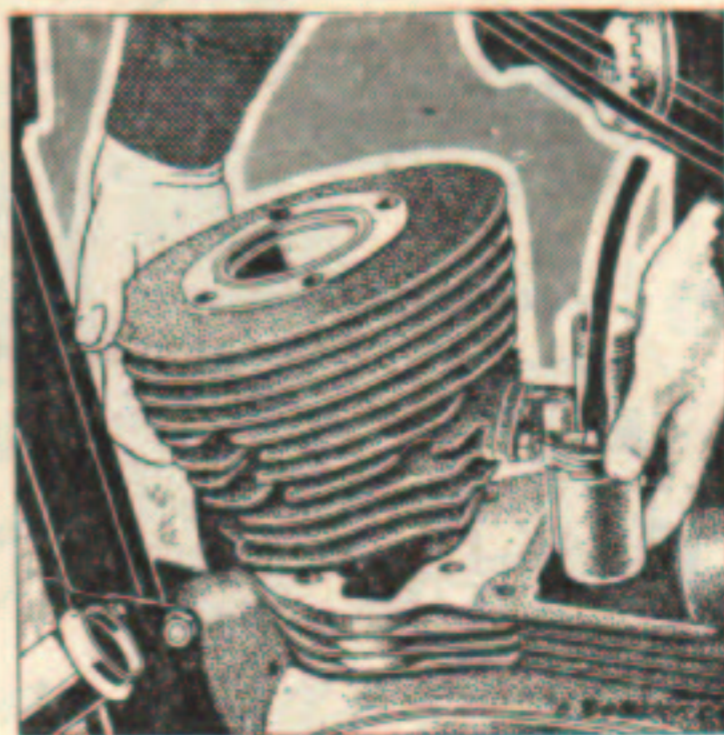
Ausschrauben der Bolzen 250 cm³
